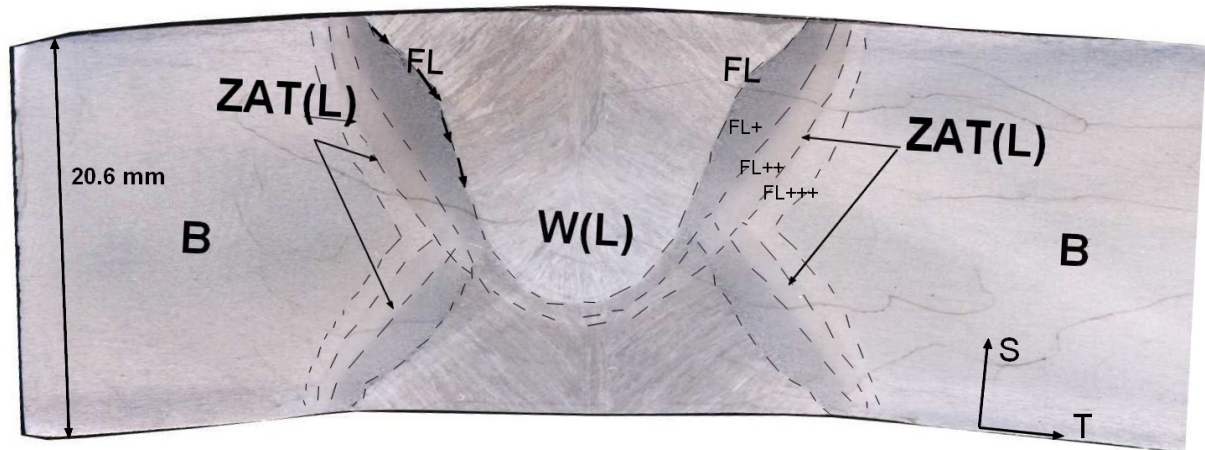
Vue macroscopique d'une coupe de la soudure longitudinale 2B50, polie et attaquée Nital
